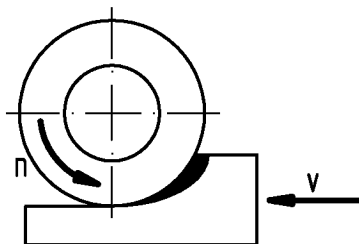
Frézování frézou s vyměnitelnými destičkami [20]
